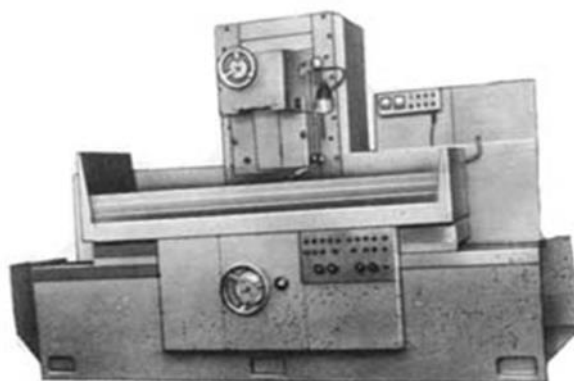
Плоскошлифовальный станок 3Д722Ф1
